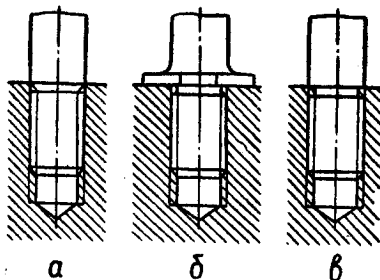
Способи забезпечення нерухомості шпильок у корпусі деталі
